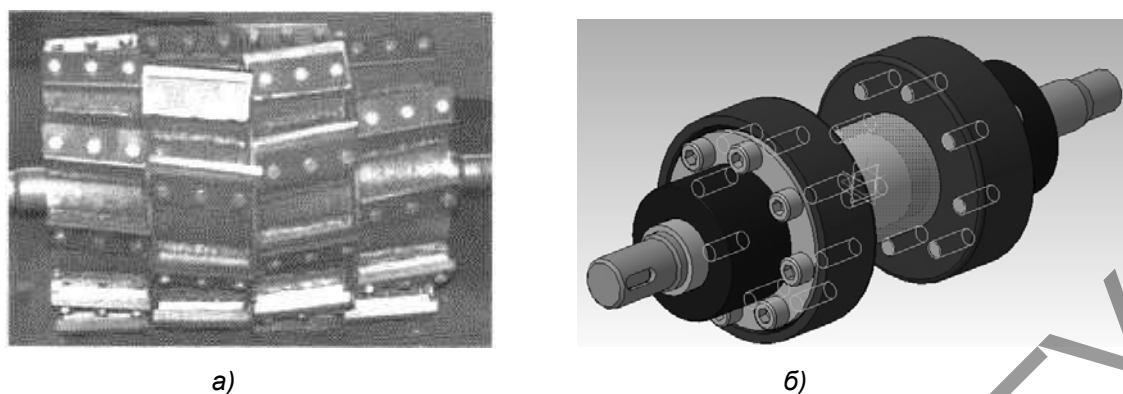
Конструкция барабана (а) и 3D-модель вала барабана с подшипниковыми опорами (б)
